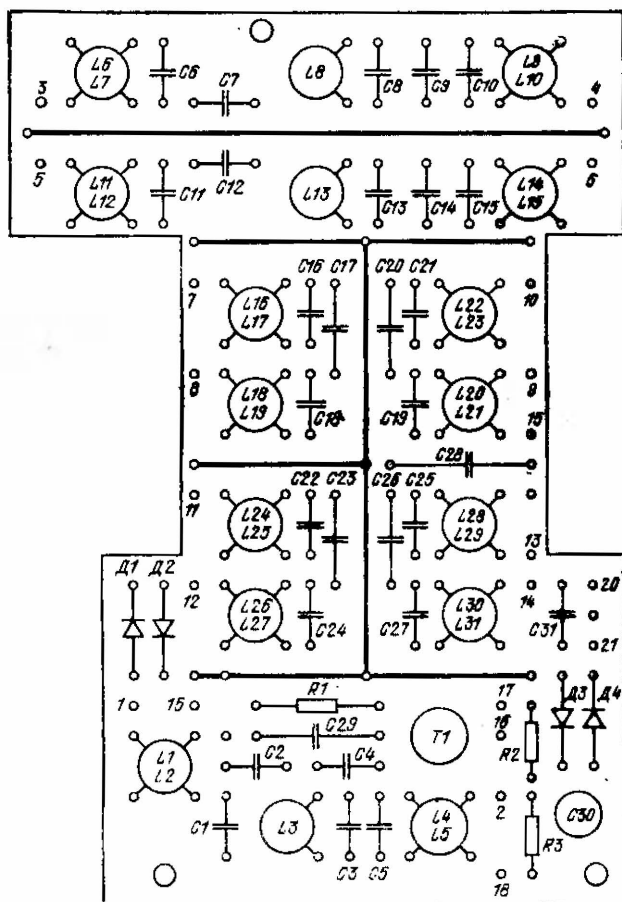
Монтажная схема платы усилителя ВЧ (вид сверху)
